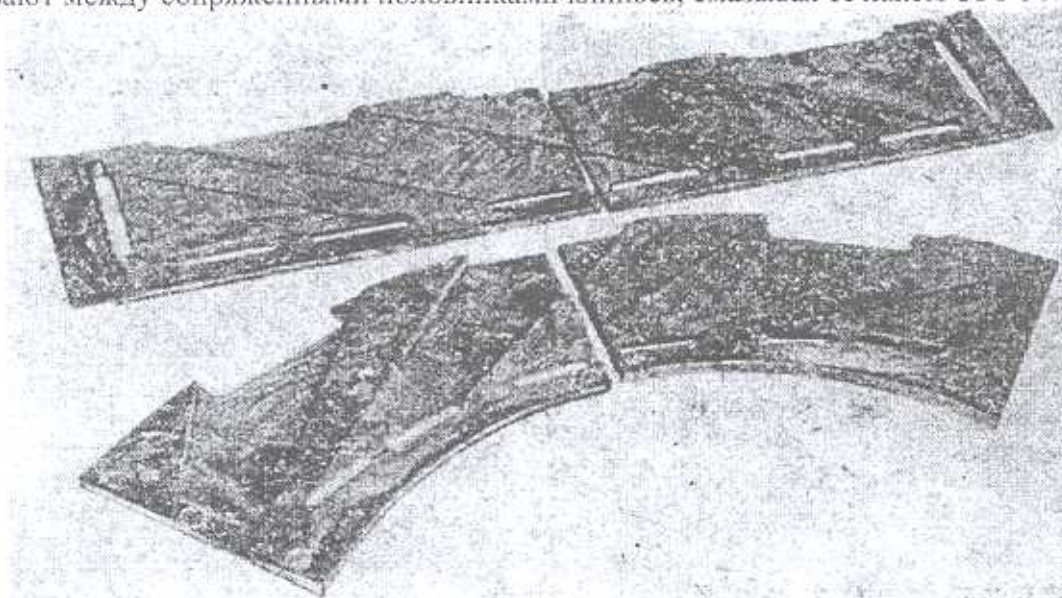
Детали расклиновки с каналами для охлаждающего газа
